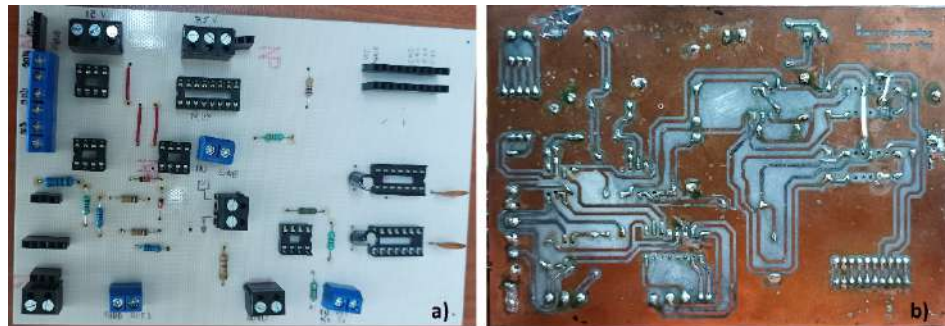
Vista de la PCB, a) componentes, b) pistas.
